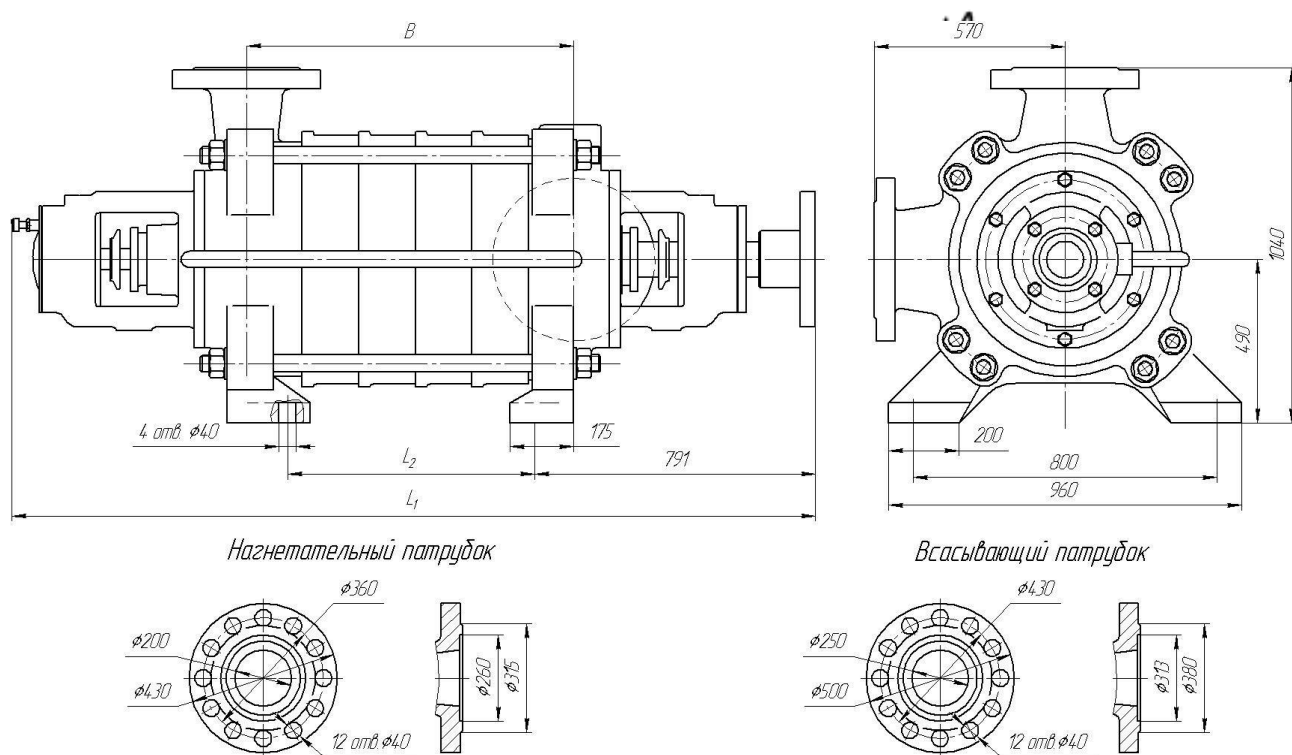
Габаритный чертёж насоса ЦНС 500-560
